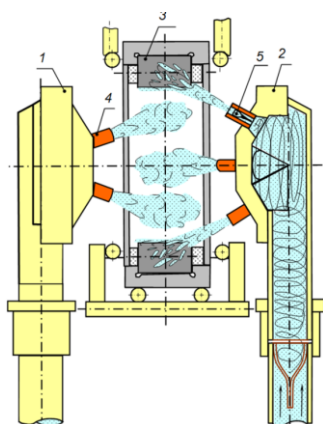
Устройство для промывки буксовых подшипников: 1, 2 – струйно-кавитационные головки; 3 – промываемый подшипник; 4 – сопла; 5 – кавитатор
